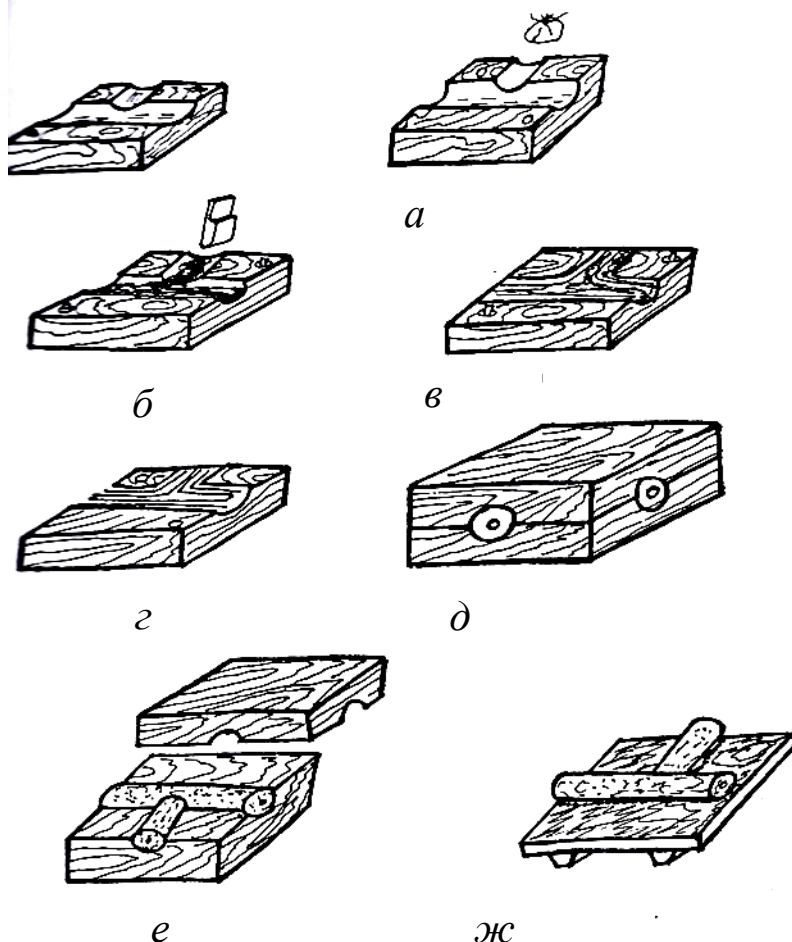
Схема технологического процесса изготовления стержня: а – ж – этапы изготовления
